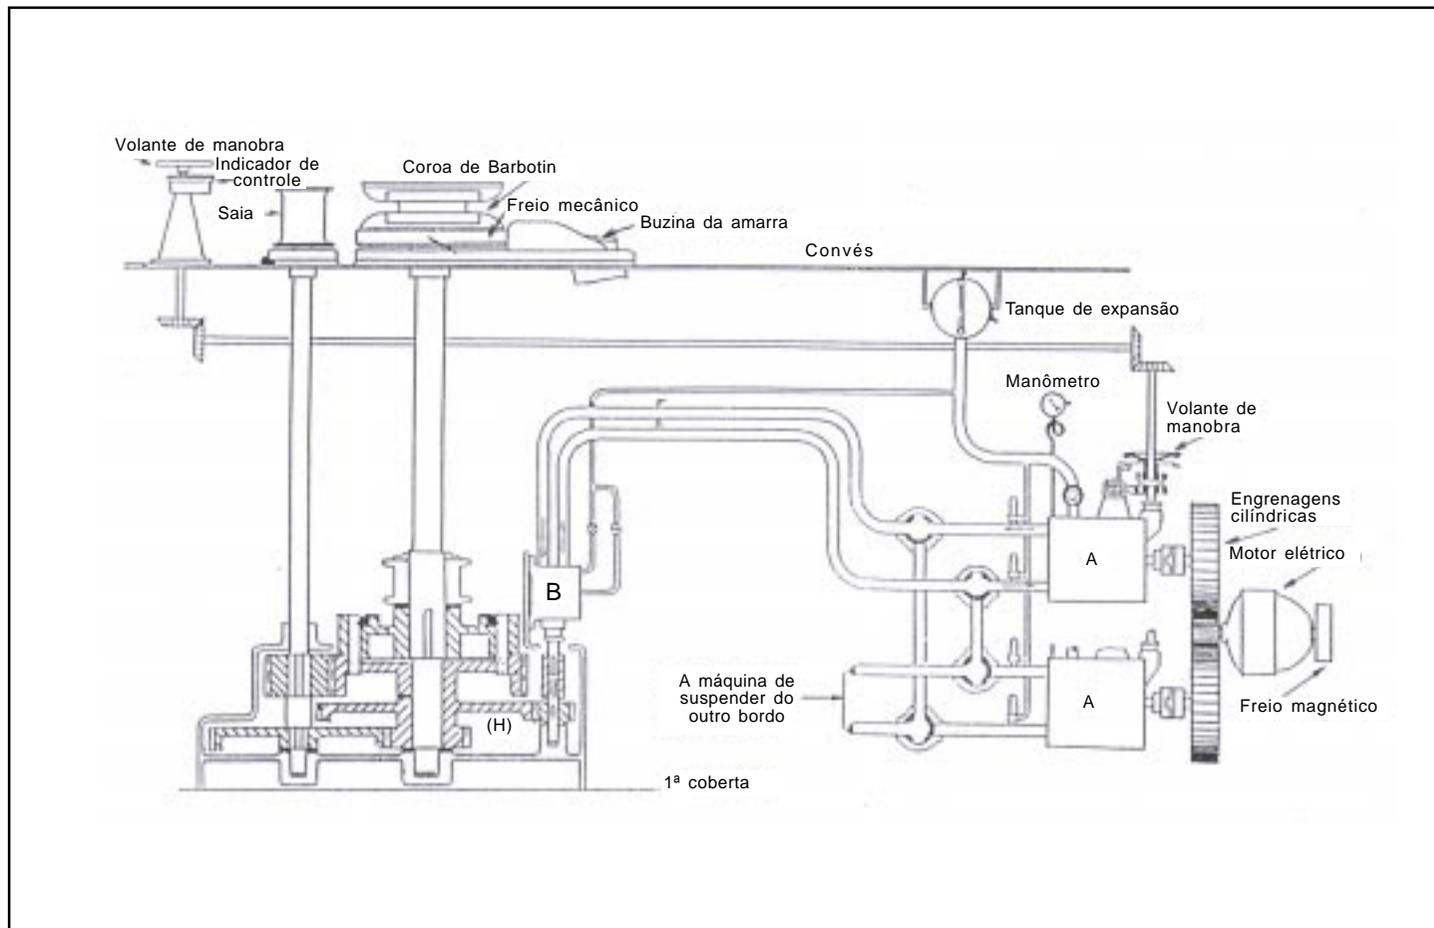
Máquina de suspender eletro-hidráulica
